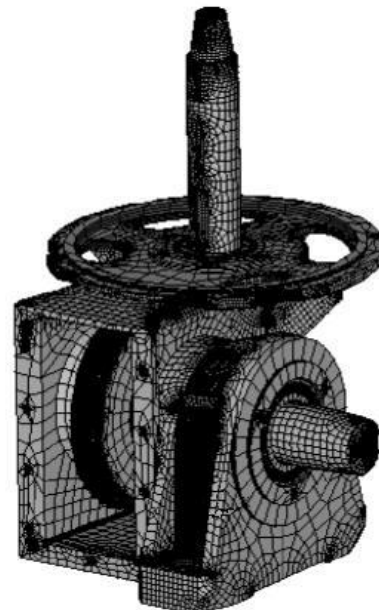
Модель для численного анализа червячного редуктора для привода с горизонтальным расположением электродвигателя.
